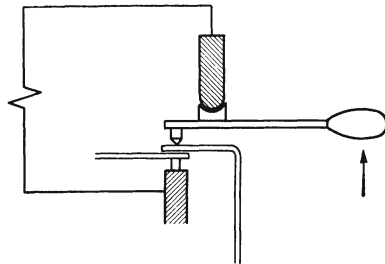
Schweißknüppel, handbetätigt.
